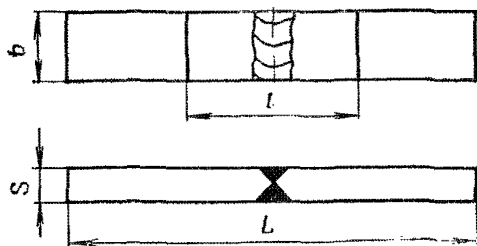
Форма и размеры плоского образца (разновидность), подготовленного для испытания сварного шва на загиб
